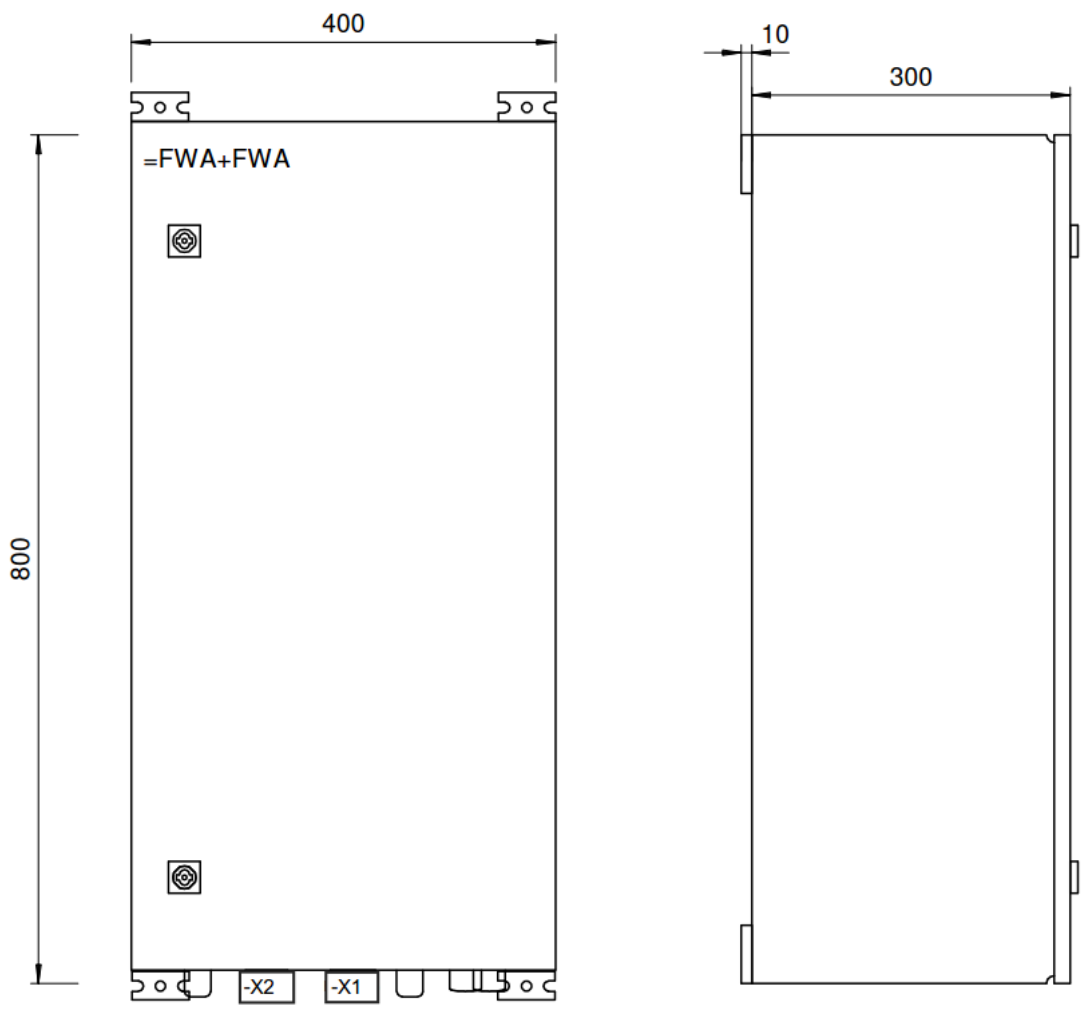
Maße und Befestigung Fernwirkschrank
